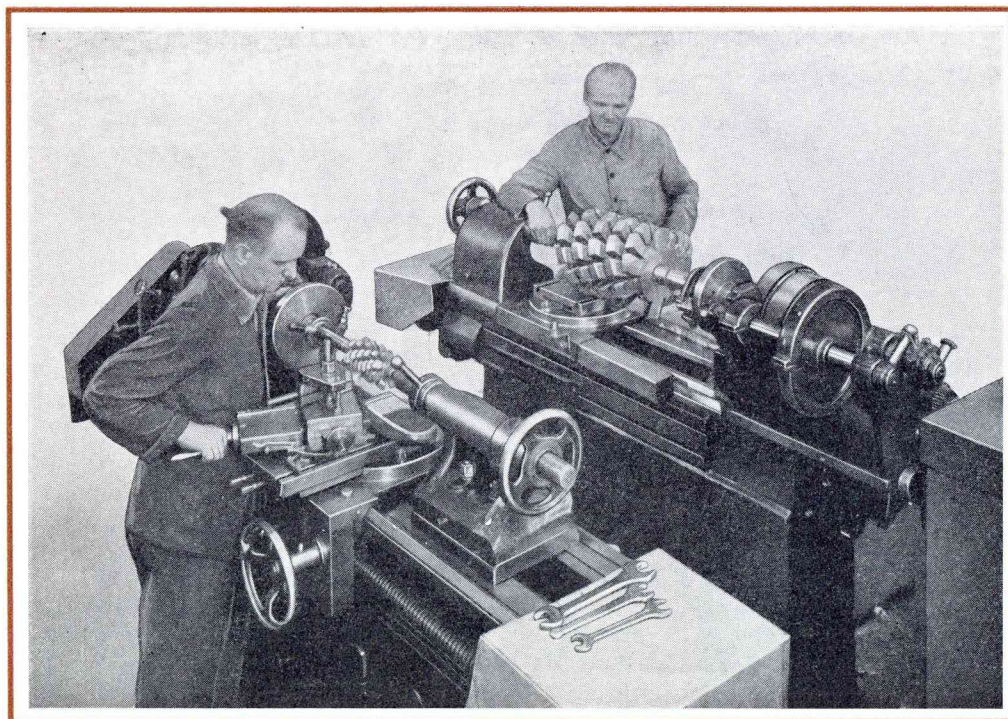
viser en drejbænk, der oprindeligt var indrettet for remtræk med trappeskive, forlagstøj o. s. v. Som det ses, er bænken nu udrustet med gearmotor og kileremtræk, hvorved ydeevnen er forøget med 50 % eller mere. Selve gearet — se fig. 107 — giver, som det ses, 4 hastigheder frem og bak og med polomkøbelbar motor 8 hastigheder.
